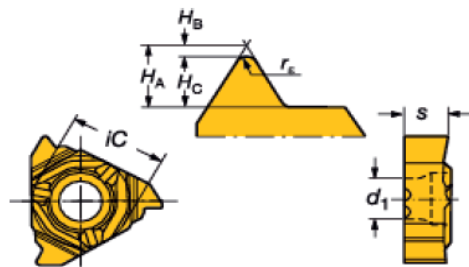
Різальна пластина для обробки методом копіювання
